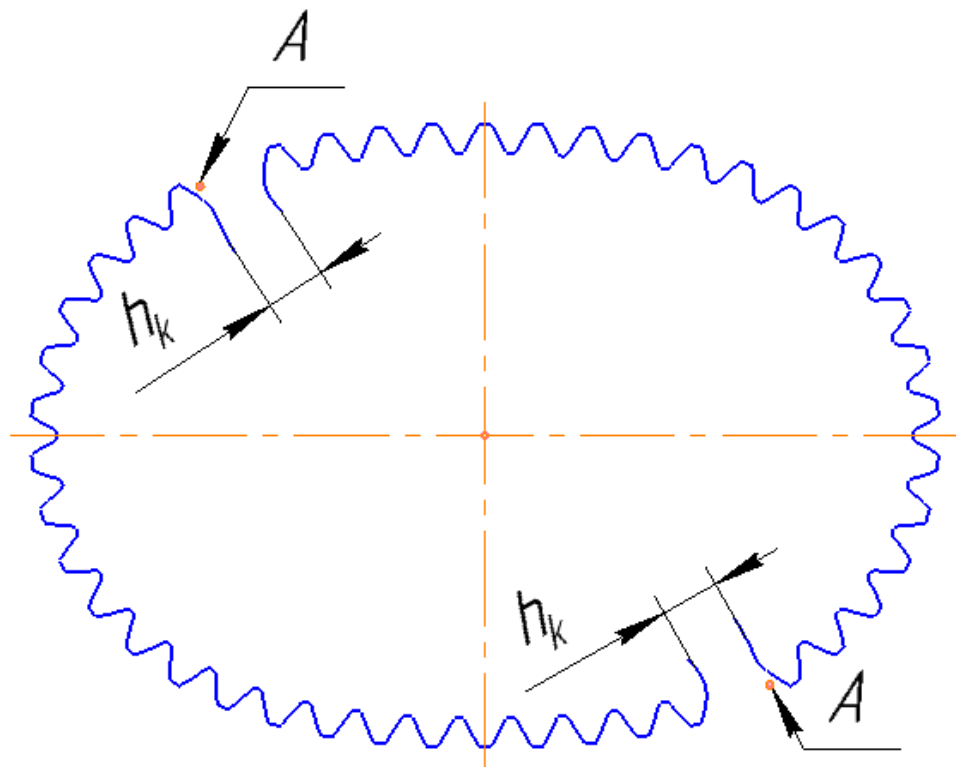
Солнечная шестерня ПРМ 3-2 с каналами в цилиндрической зубчатой поверхности
